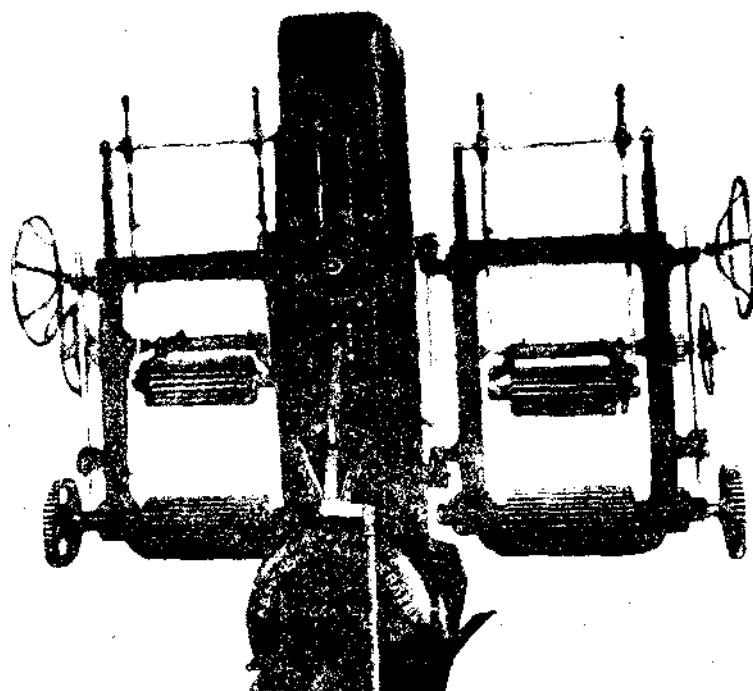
Лесопильный рамный станок с открытыми обеими вальцевыми рамами.
